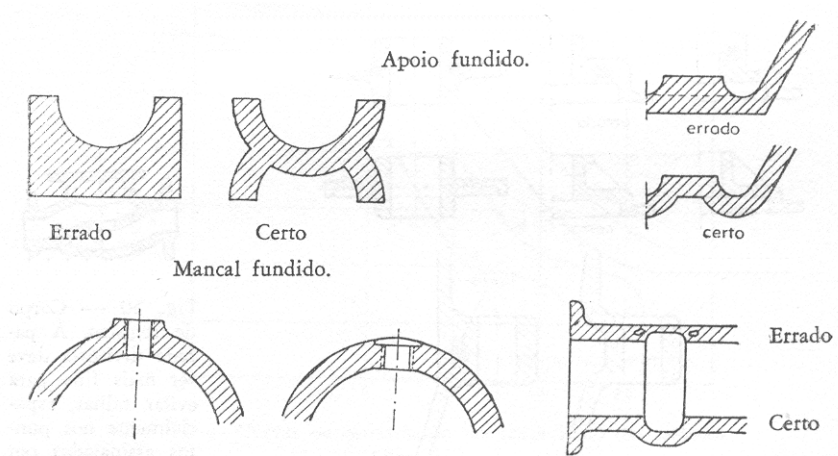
Exemplos de aplicação de paredes uniformes - 1.
